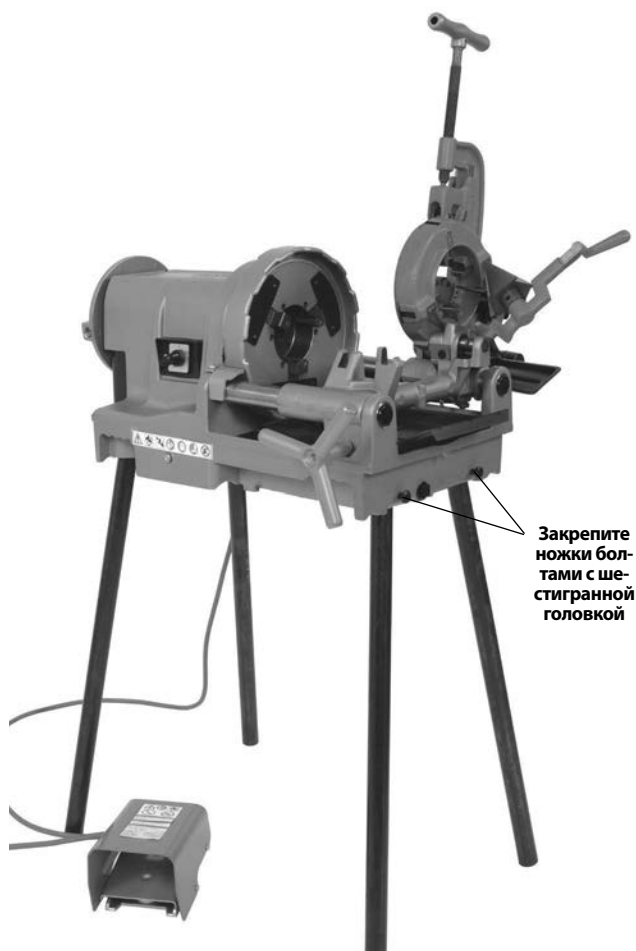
Установка резьбонарезного станка на трубные стойки
